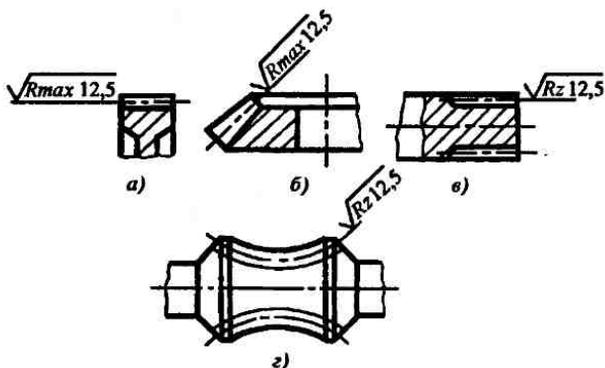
Обозначение шероховатости поверхности зубьев детали без указания их профиля и глобоидных червяков
